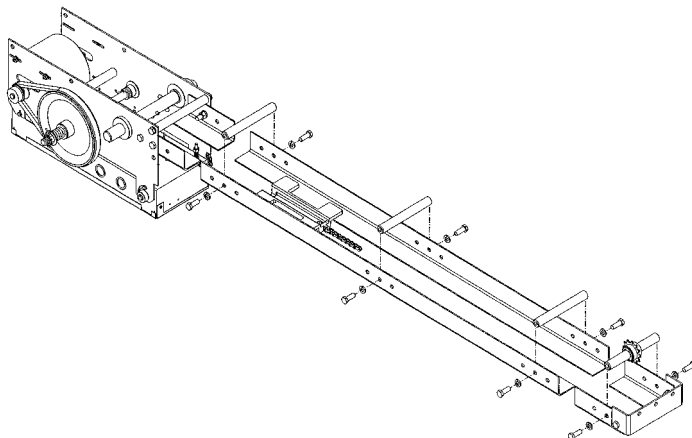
Assemblage de l'ouvre porte sur les rails
